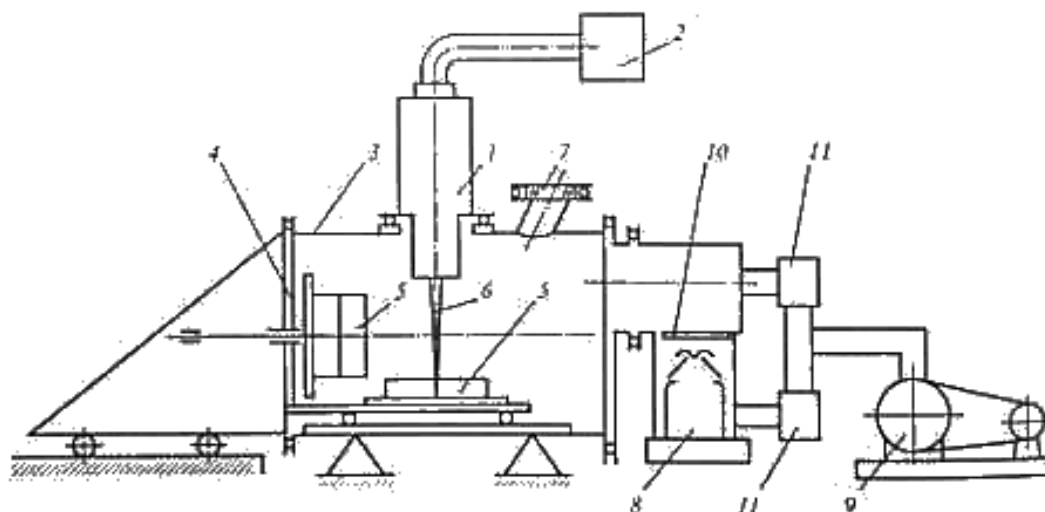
Схема установки для электронно-лучевой сварки:
